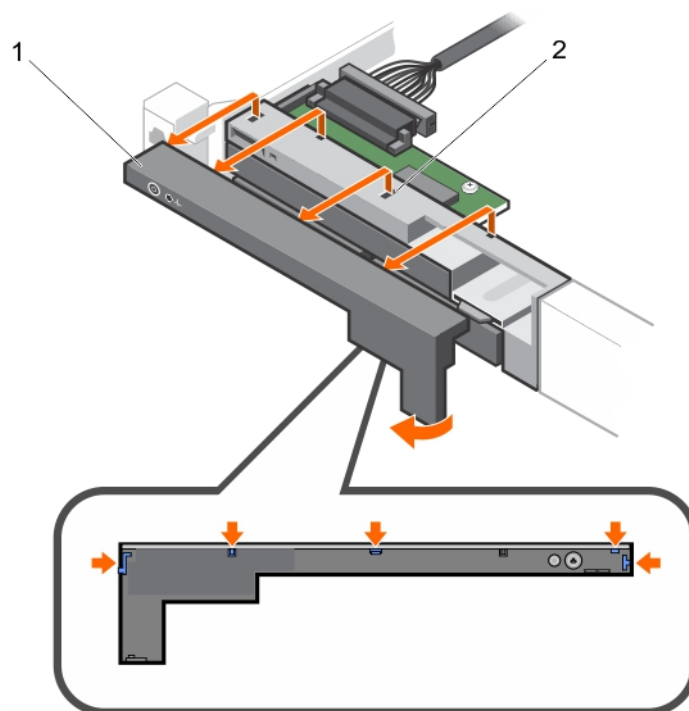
Entfernen des Bedienfelds – Gehäuse für acht 2,5 Zoll-Festplatten
